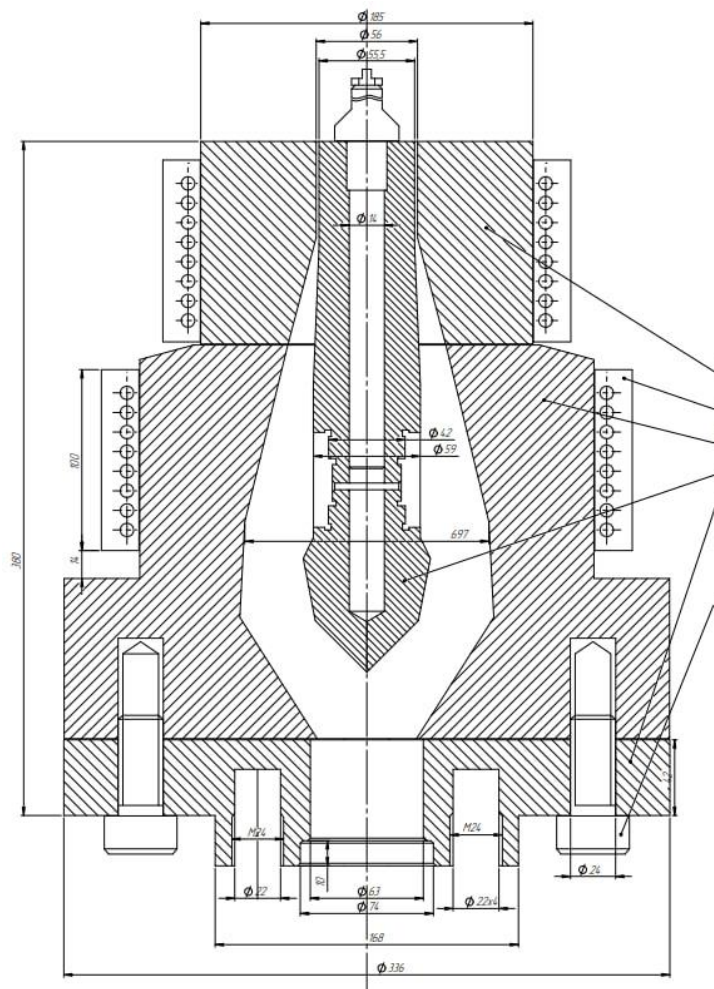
Конструкція головки для виробництва плівки рукавної:
